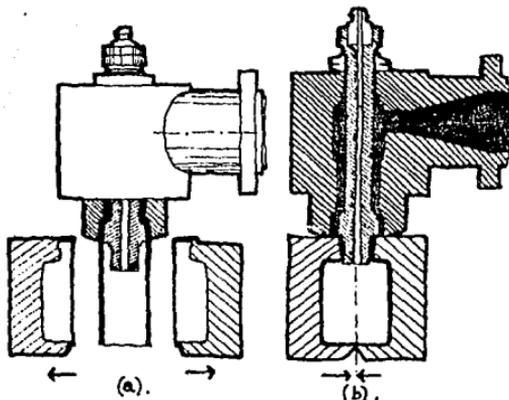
Corte simplificado de un juego de cabezal y dado, a).- Su posición durante la extrusión del parison y b).- Durante el soplado.
